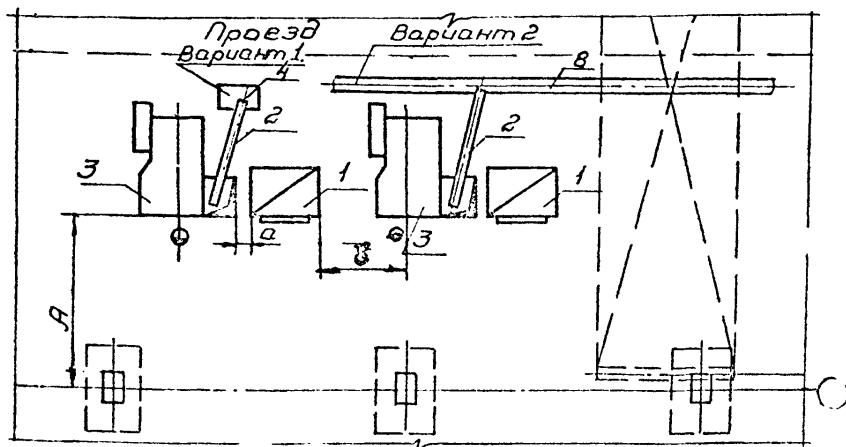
Схема расположения штамповочных линий на базе ГКМ:
